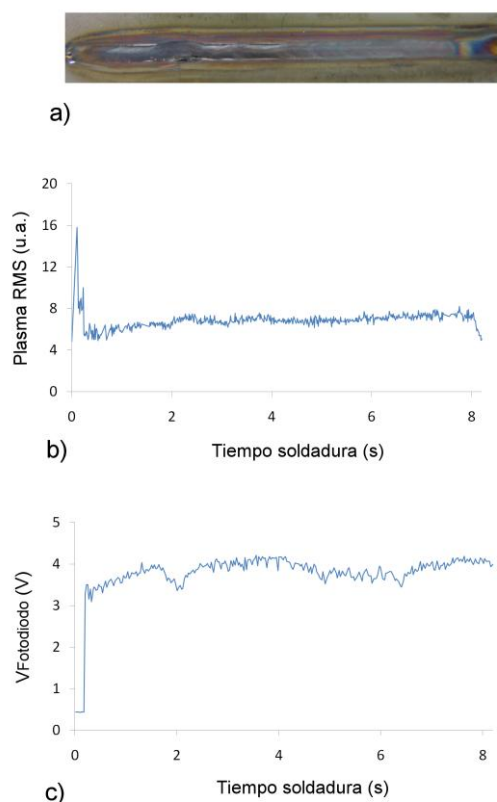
Soldadura defectuosa (chapas con diferentes espesores).
